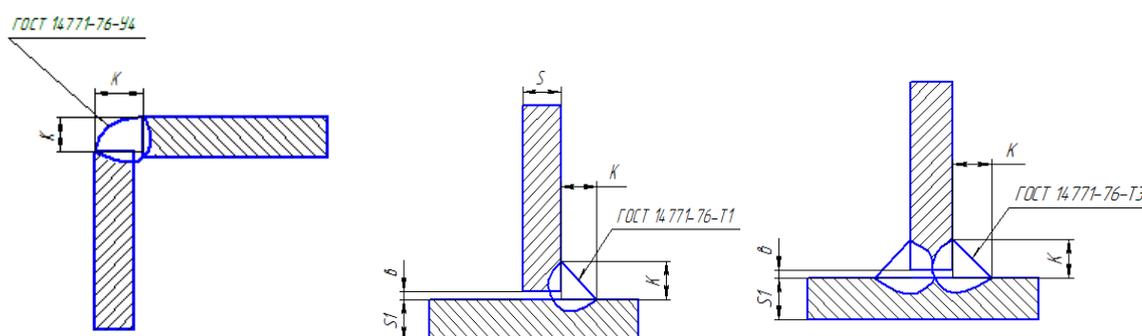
Эскиз подготовки кромок и вид сварного шва
